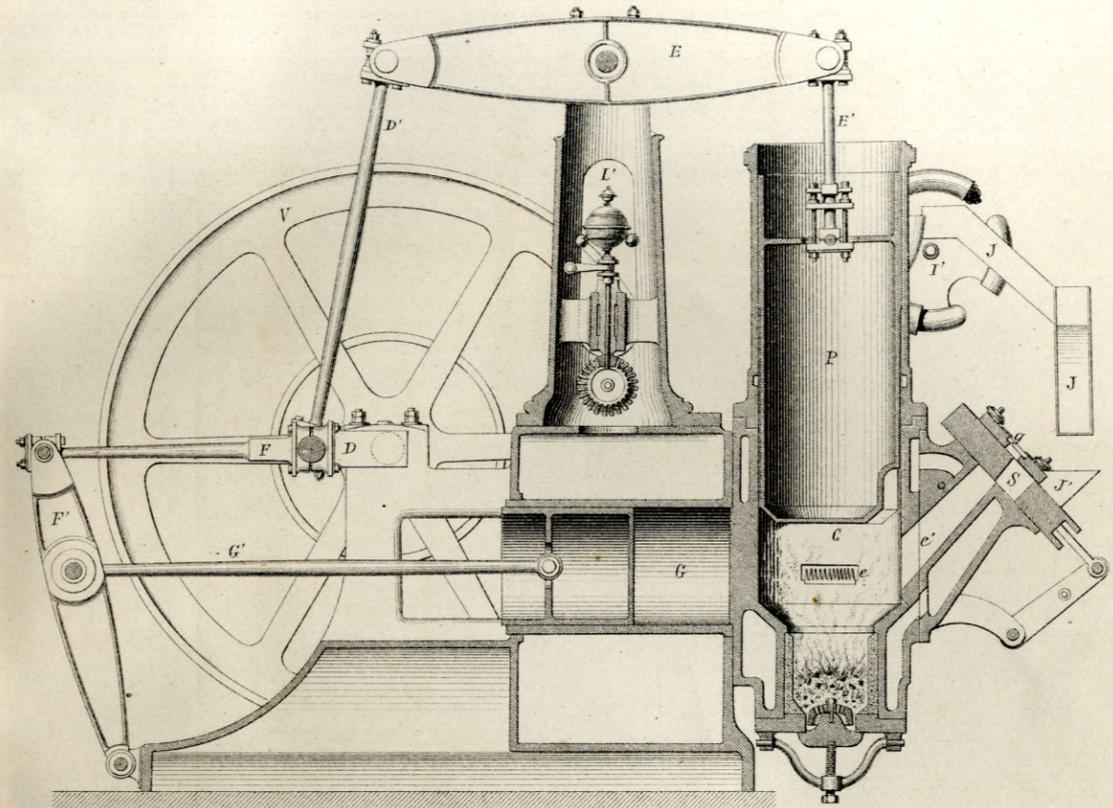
Sezione longitudinale secondo 5, 6.
